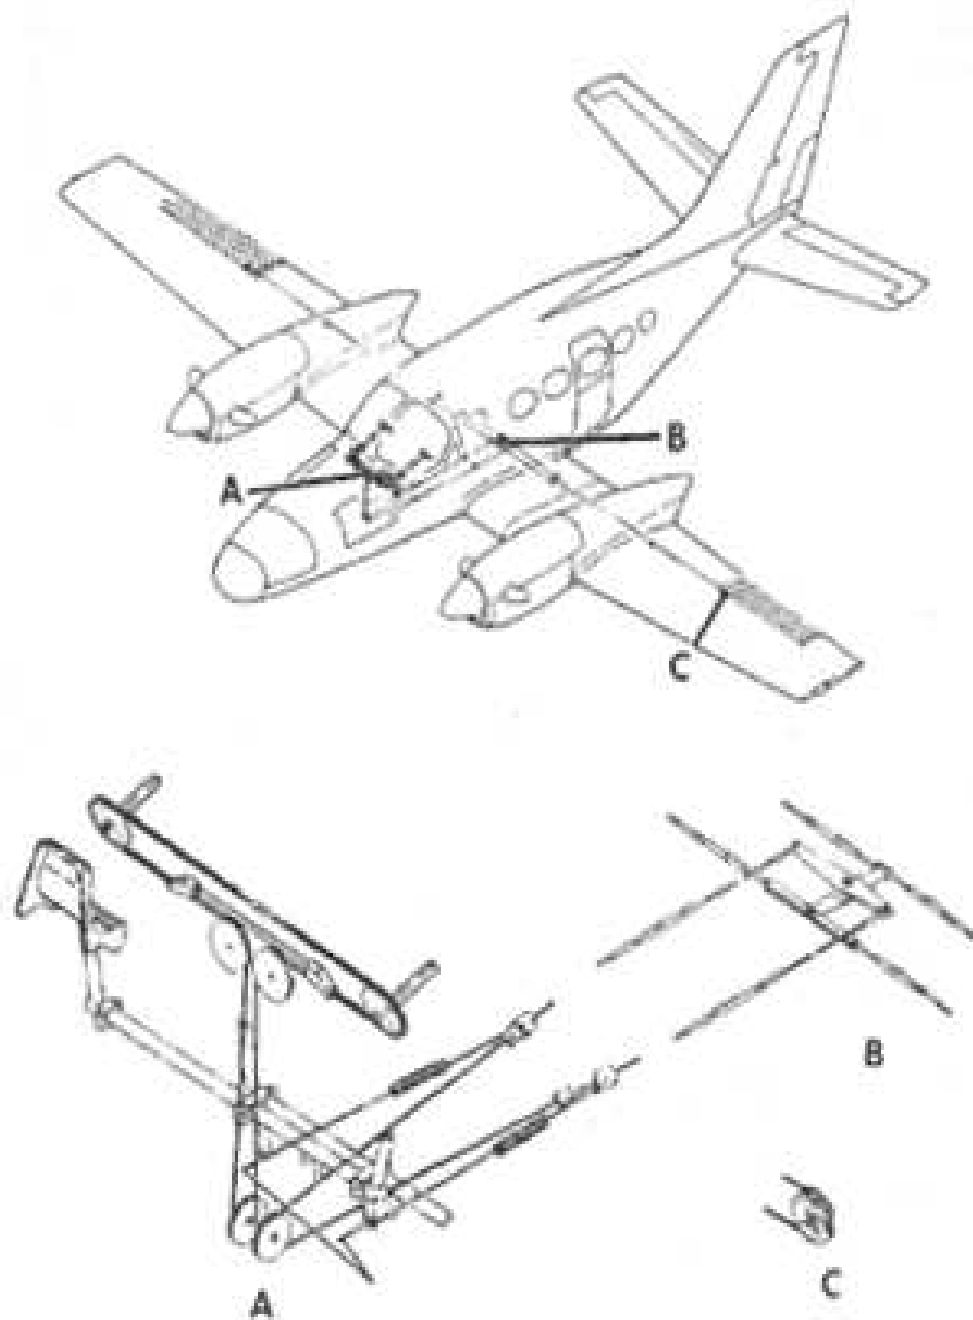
Detalle de sistema mecánico de control de vuelo (conjunto de mando de alerones).
